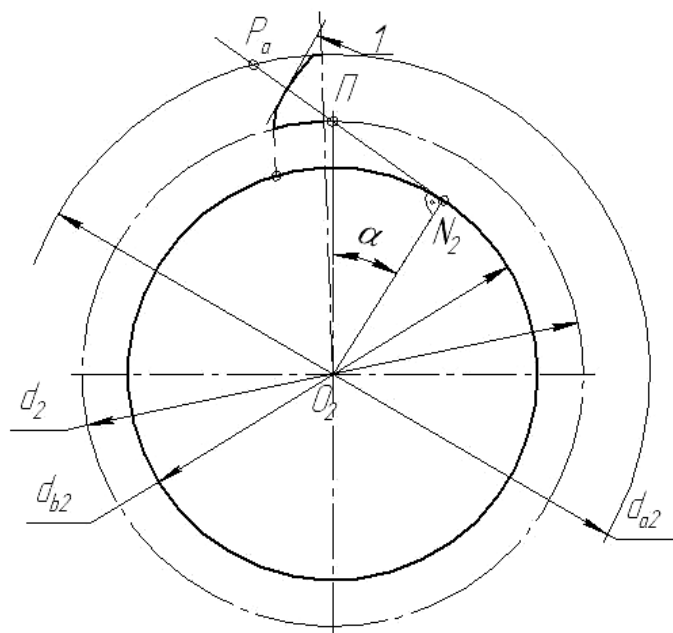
Схема для определения длины активной линии зацепления профиля головки зуба колеса с касательной к винтовой поверхности витка червяка: 1 – касательная к винтовой поверхности витка червяка; П – полюс зацепления
